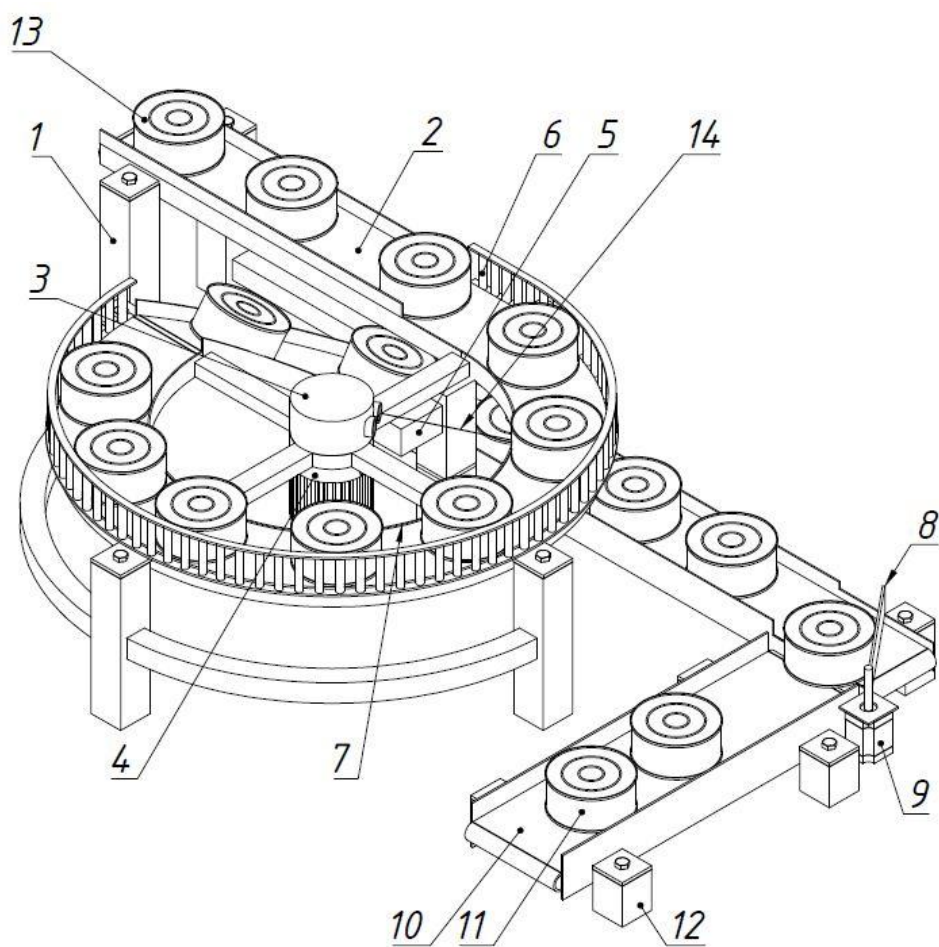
Устройство для контроля герметичности консервных банок, общий вид
